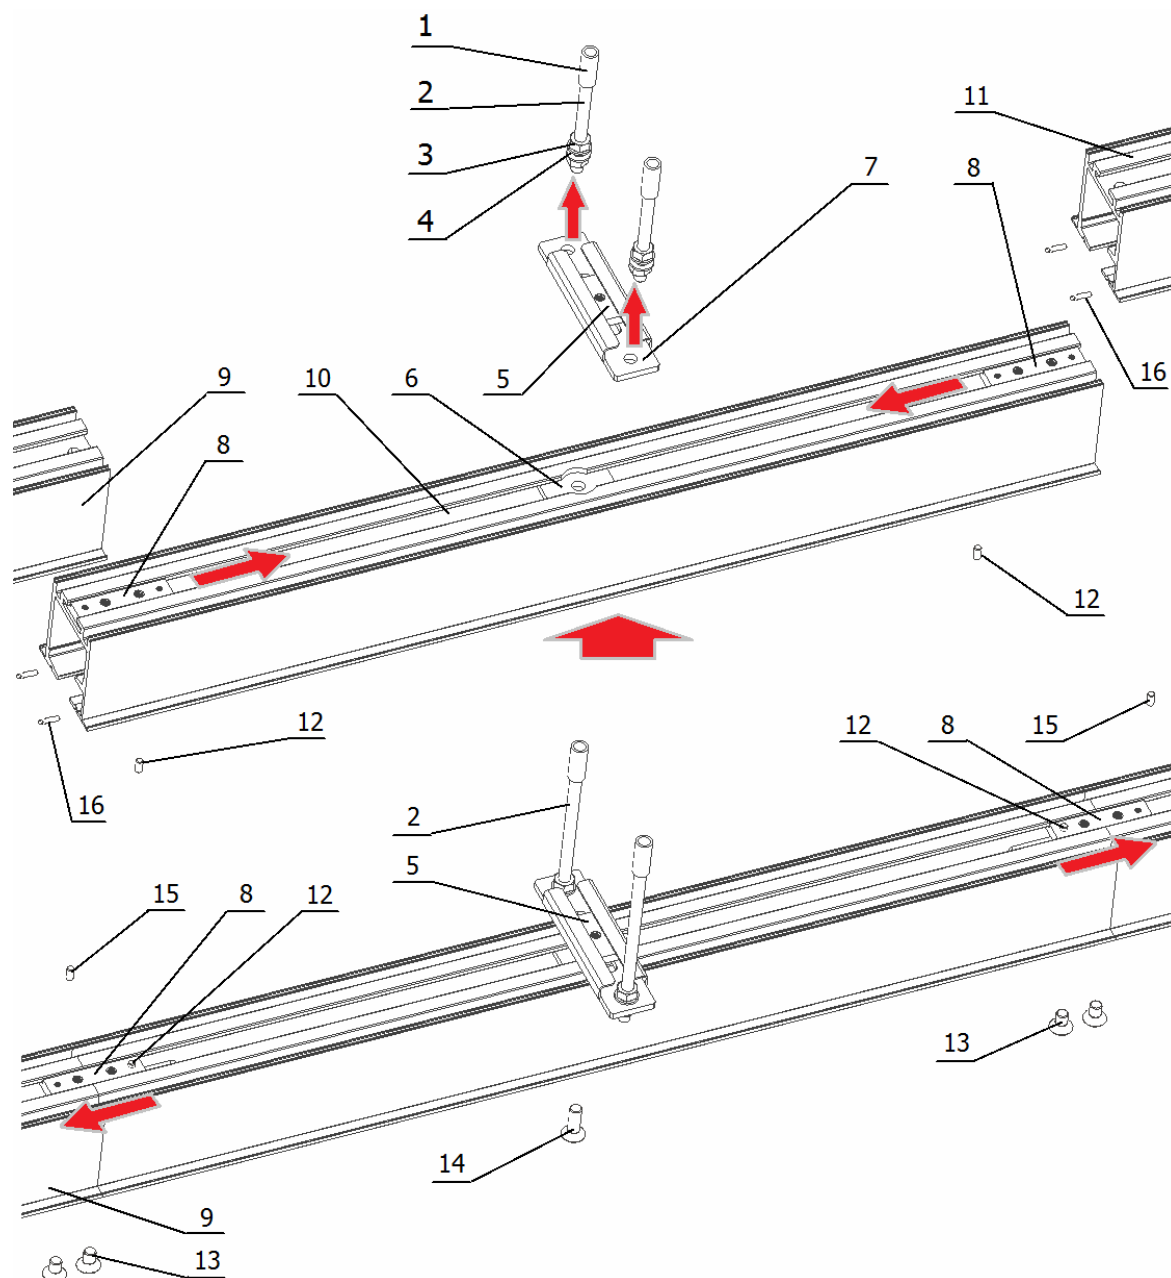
Schemat montażu modułu serwisowego dla torów 34-0150 i 34-0151
